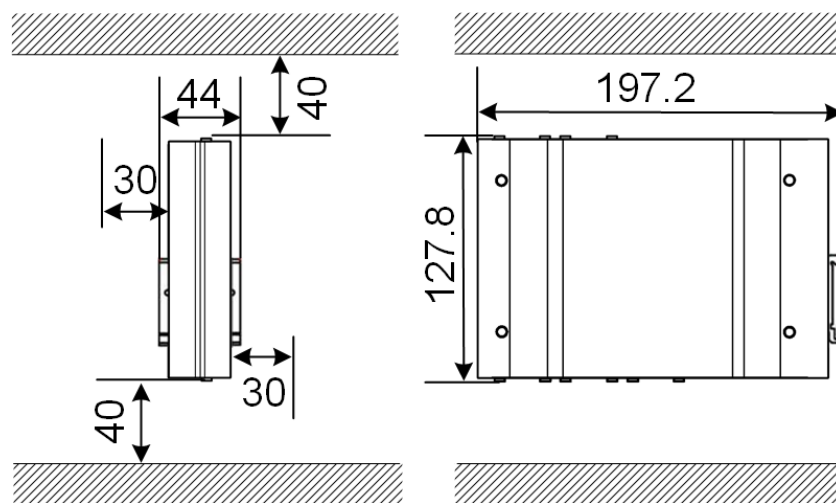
Ingombro (dimensioni in mm) in caso di montaggio nell'armadio elettrico
